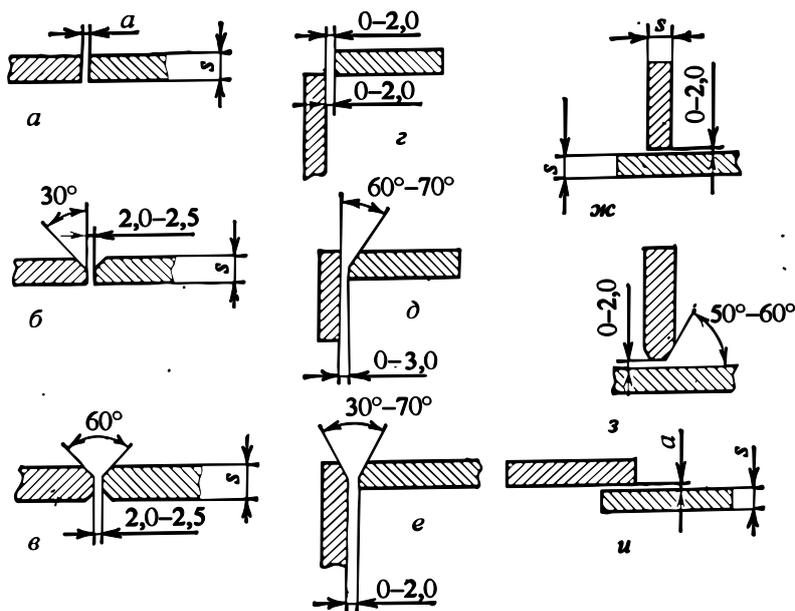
Рекомендуемые типы соединений для ручной дуговой сварки
